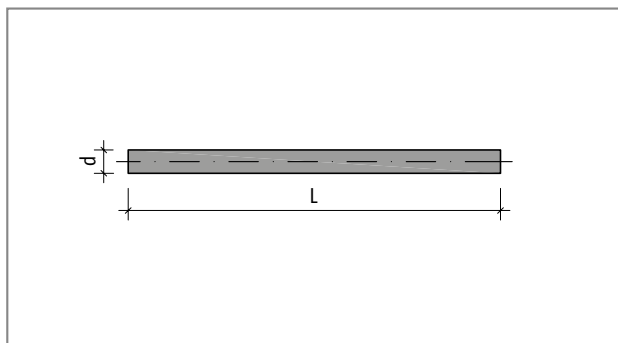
Schöck Dorn tipo LD Part A4, LD Part Zn: dimensioni del perno
